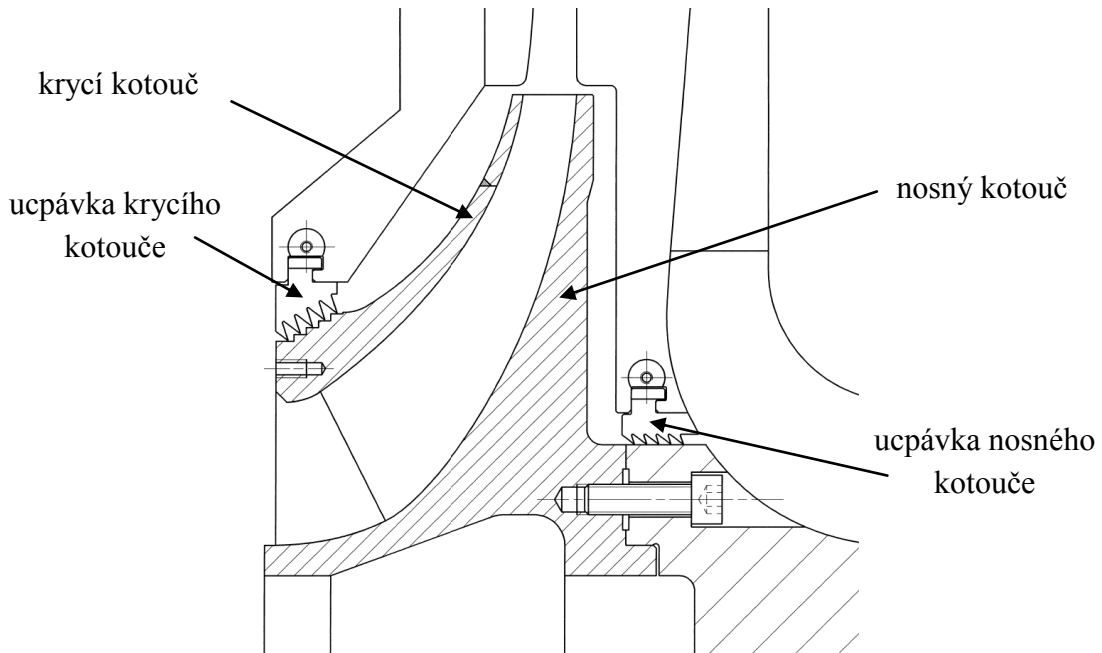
Schéma vícestupňového radiálního kompresoru - převzato z [3]
